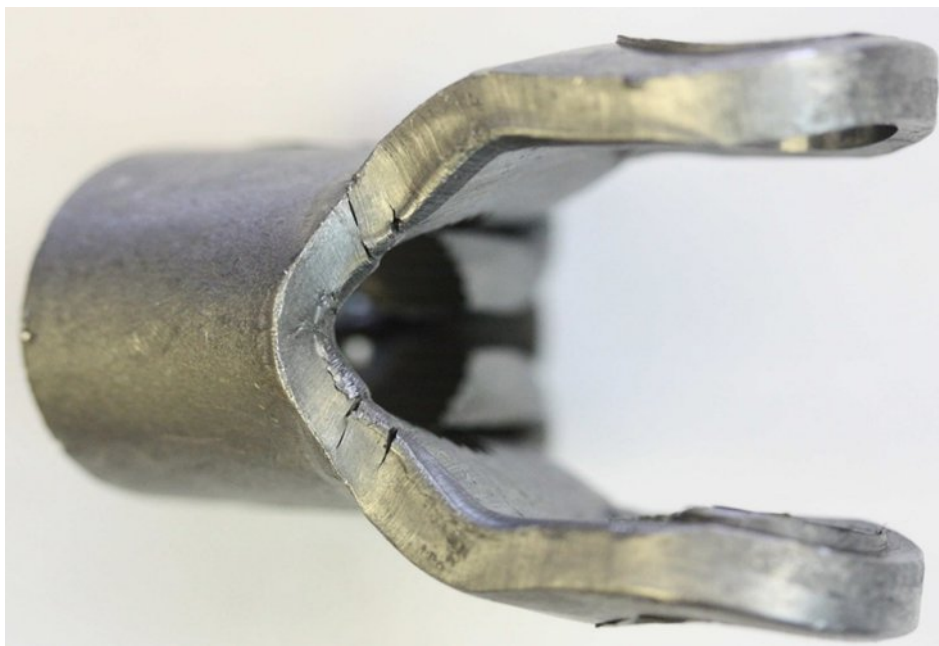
Формованная заготовка с типовыми трещинами на переходной части детали
